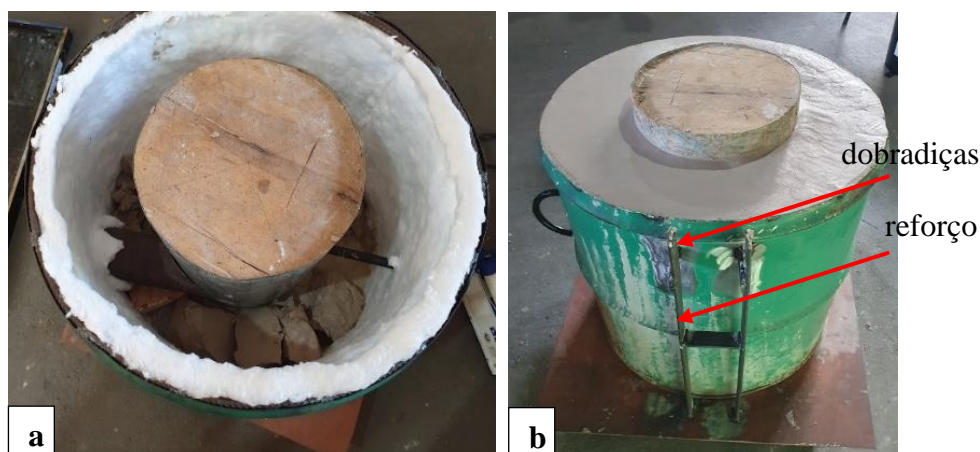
Construção da parede da câmara de combustão, (a) aplicação da manta térmica, e (b) concretagem com argamassa refratária (fonte: Autores, 2024).
